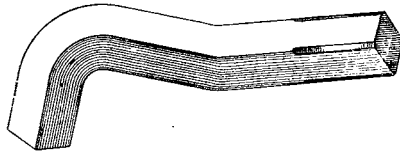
Ключ КВ-85-425 к гайке оси катка и натяжного валика главного фрикциона
